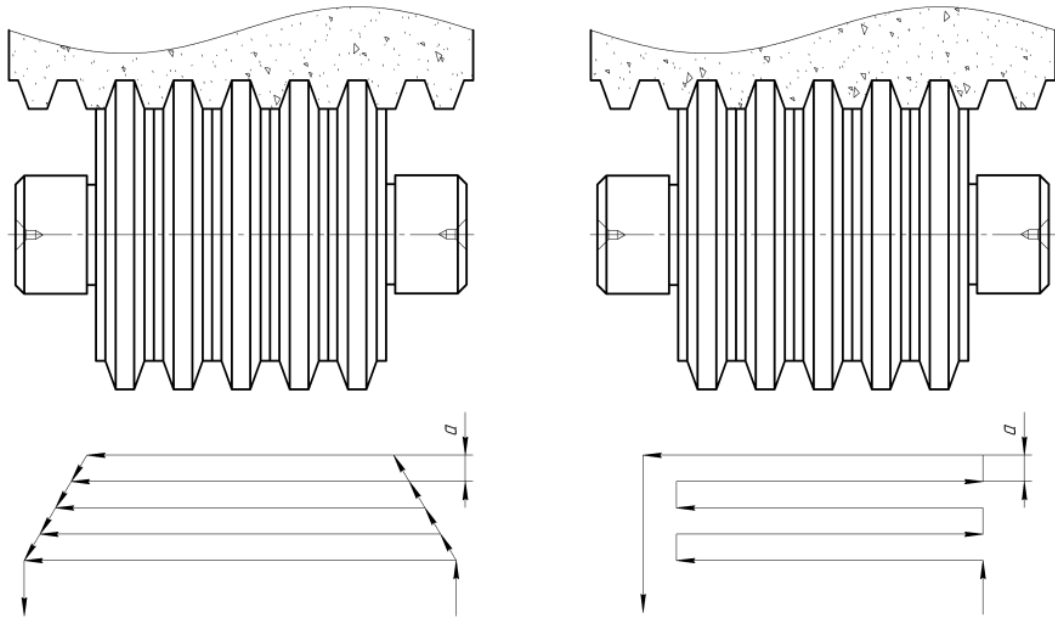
Схемы накатки червячной поверхности гиперболического шлифовального круга: а) односторонняя; б) двухсторонняя
